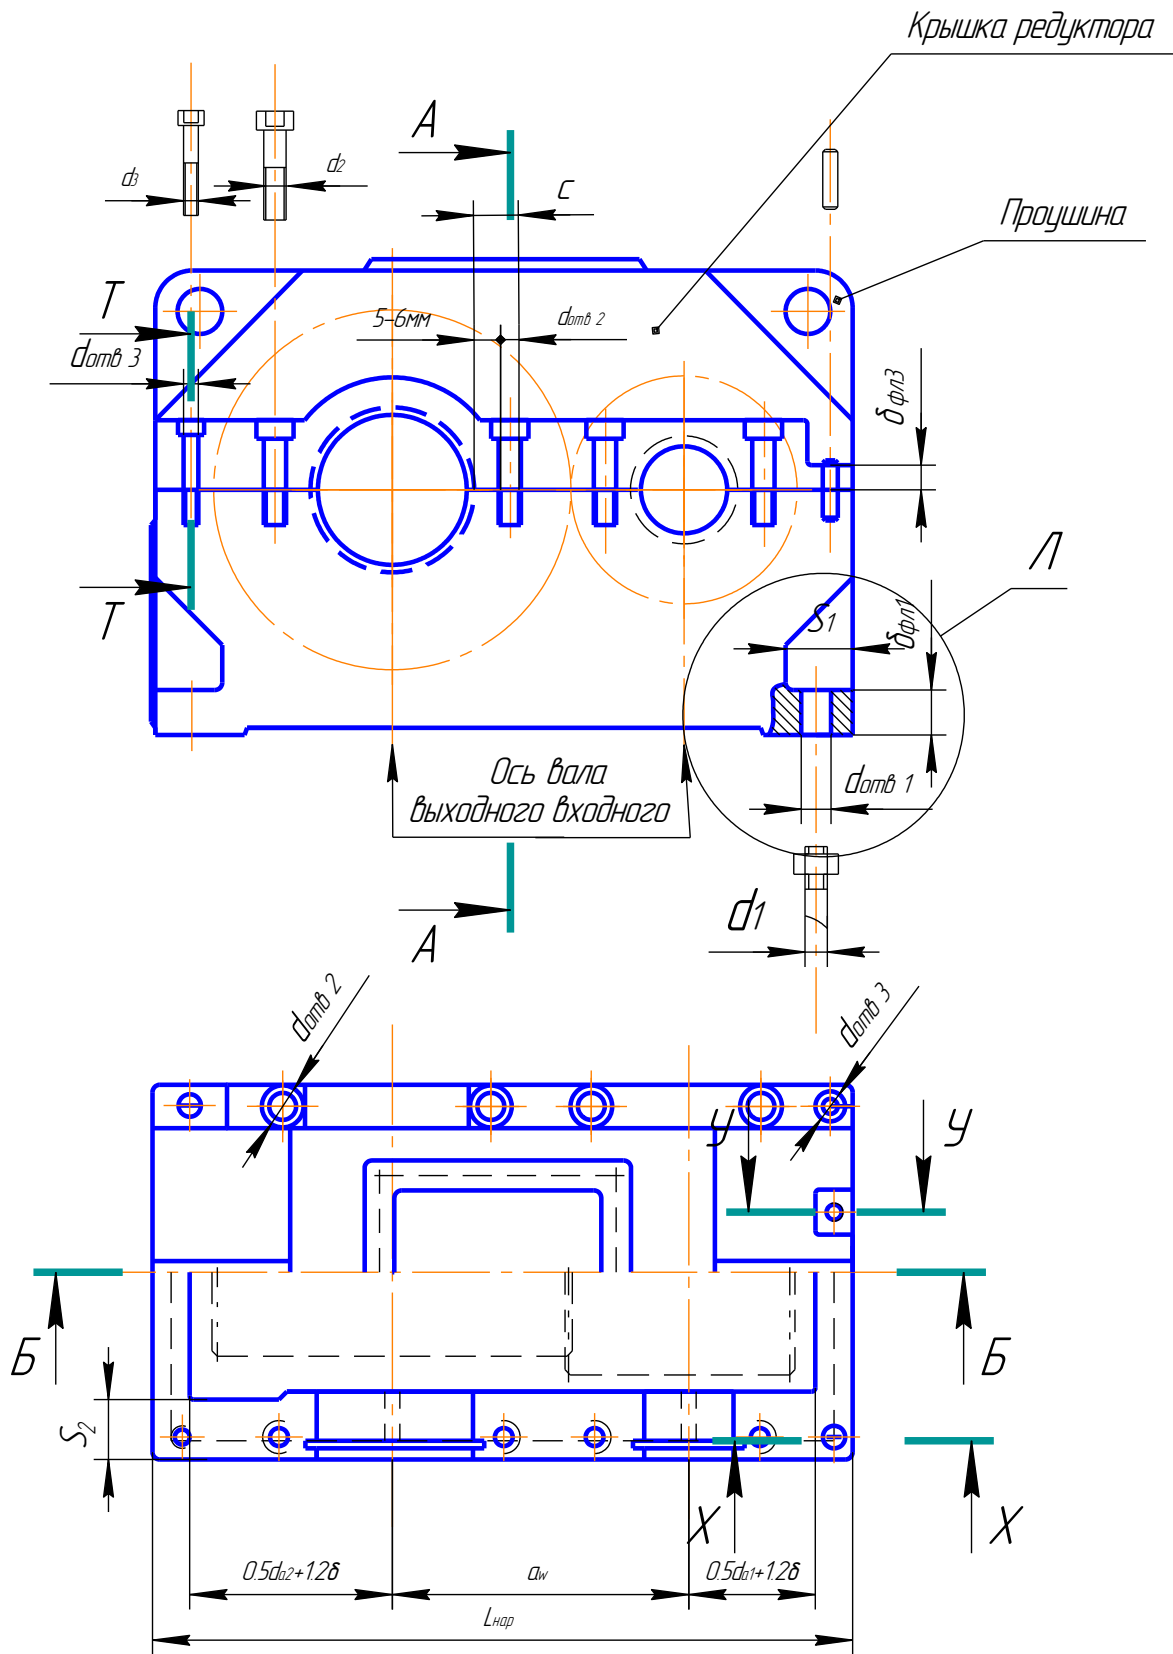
(лист 1, листов 3) Конструкции корпусных деталей цилиндрических редукторов с внутренним расположением подшипниковых бобышек
